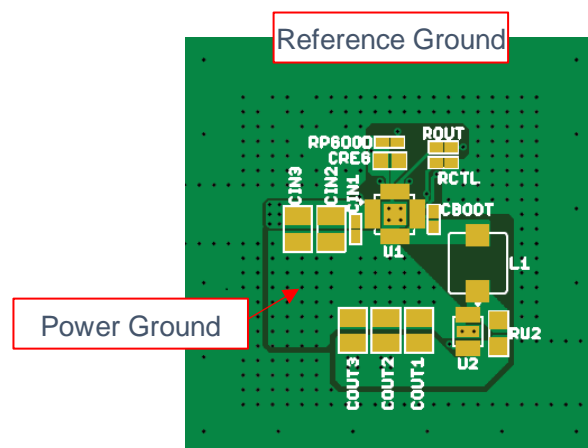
PCB レイアウト例 (昇降圧 DC/DC コンバータ)
